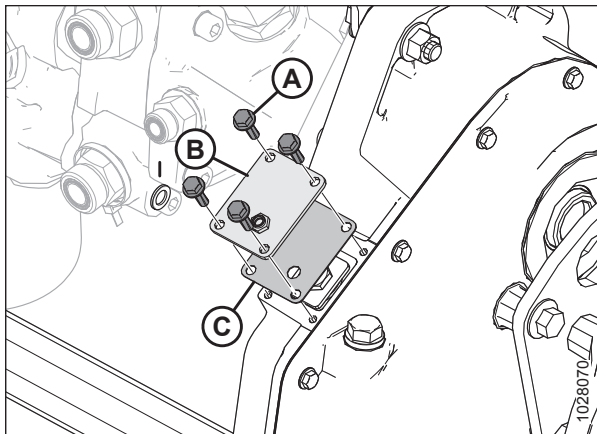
Cubierta del tensor de la cadena de la caja de engranajes principal
